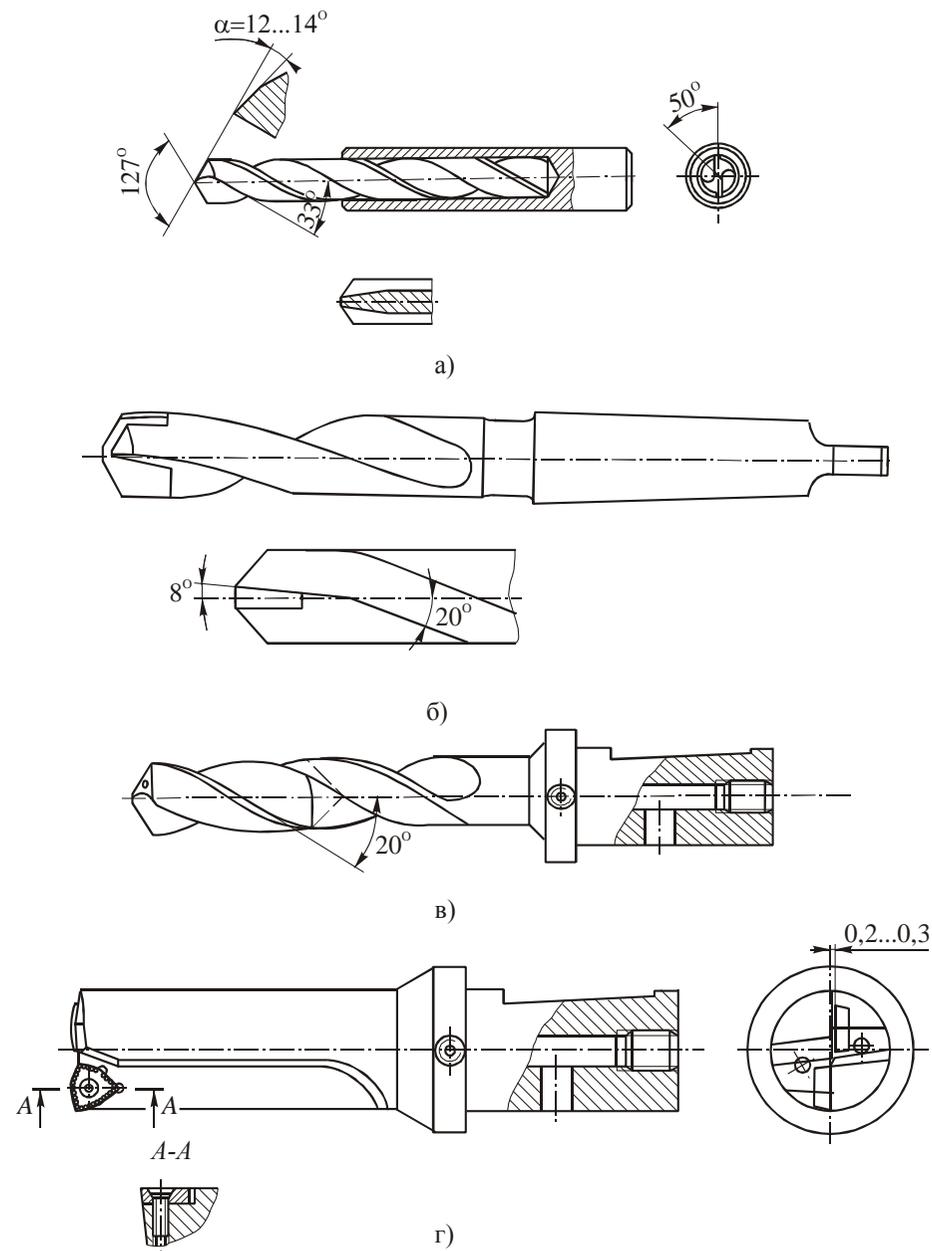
Твердосплавные сверла: *a* – цельные; *б* – с напайными пластинами; *в* – с коронками; *г* – с механическим креплением СМП
